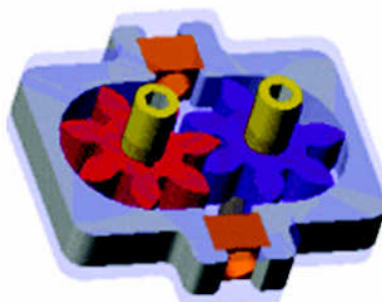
Máquina de deslocamento rotativa de engrenagens
